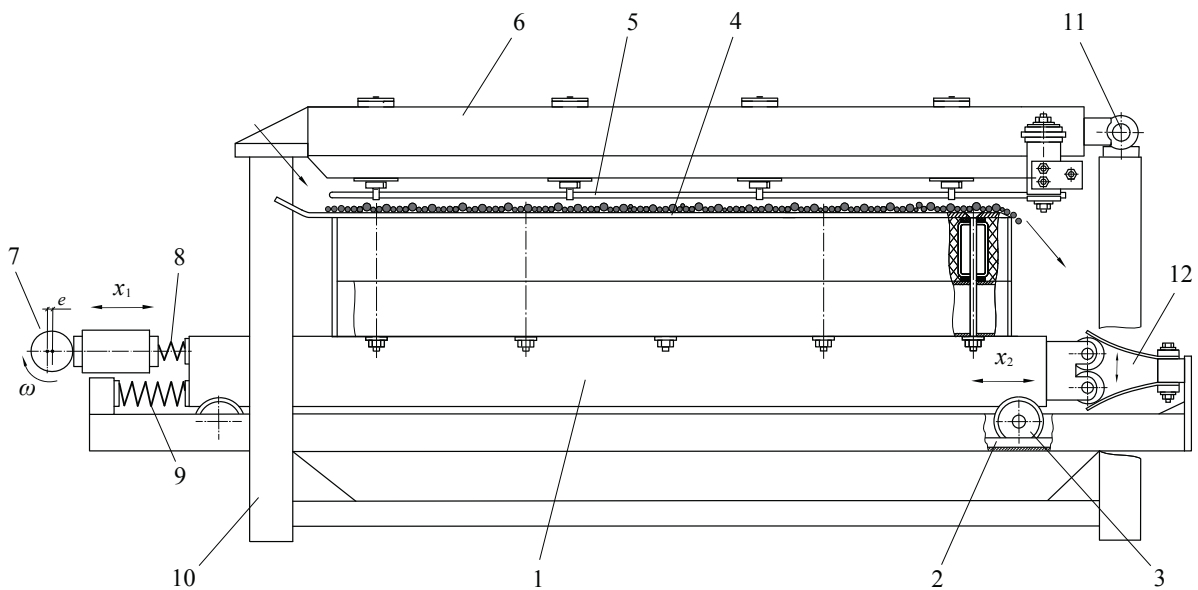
Электрическая печь с горизонтальной подовой платформой: 1 – платформа; 2 – направляющие; 3 – подшипники; 4 – подовая плита; 5 – электронагреватели; 6 – термокрышка; 7 – эксцентриковый привод; 8, 9 – пружины; 10 – рама; 11 – шарнир; 12 – нелинейный упругий элемент
